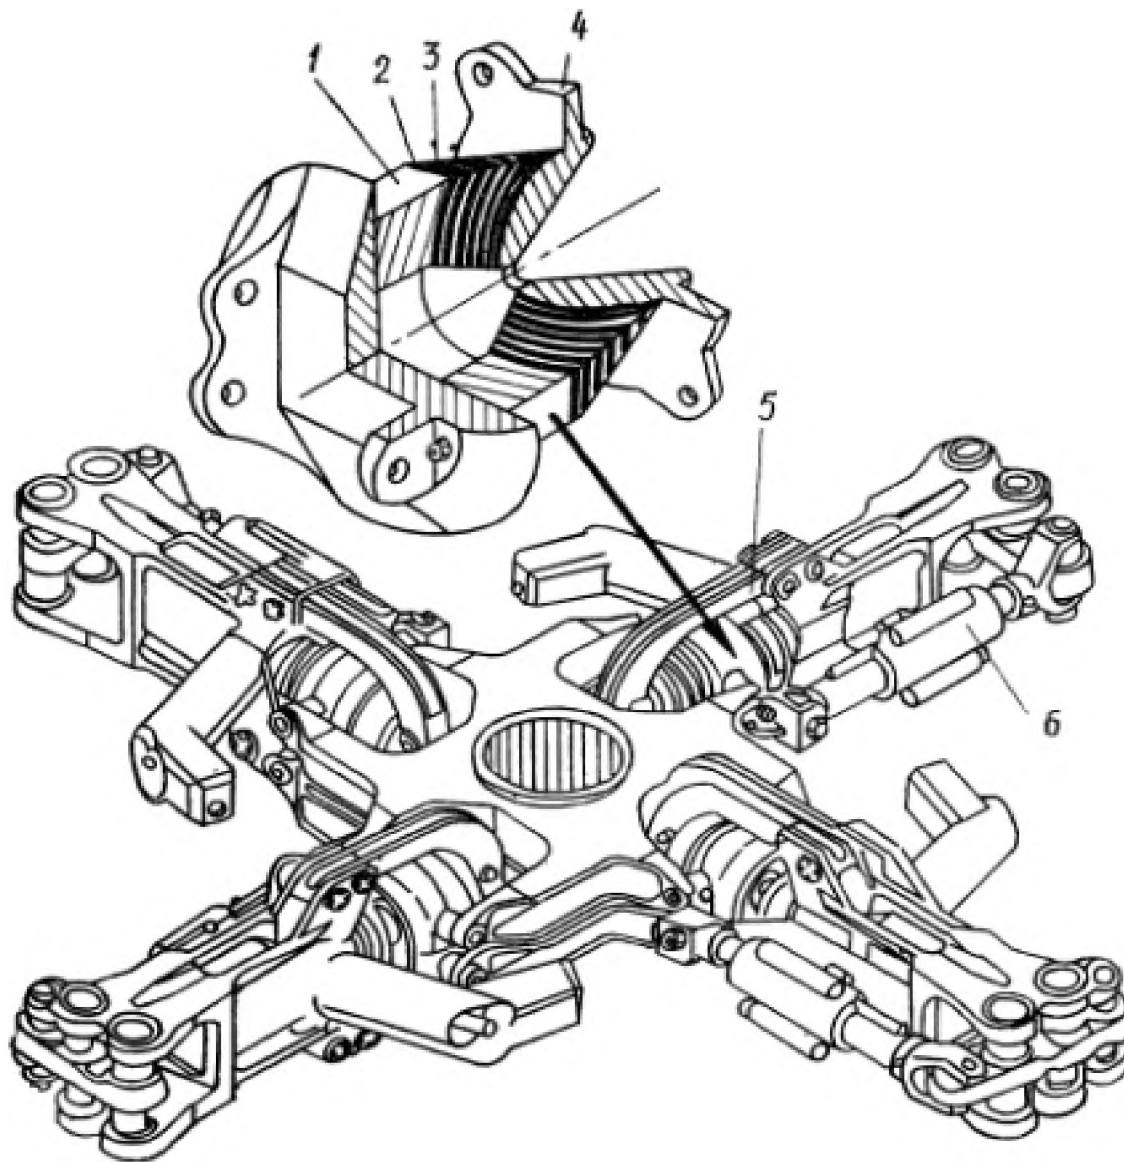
Втулка НВ с эластомерными подшипниками [3]:
